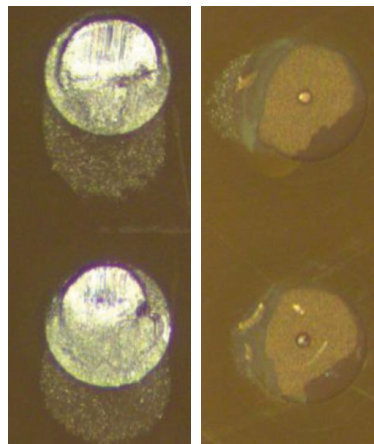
Aspect visuel du BGA sur assemblage par BB305.
